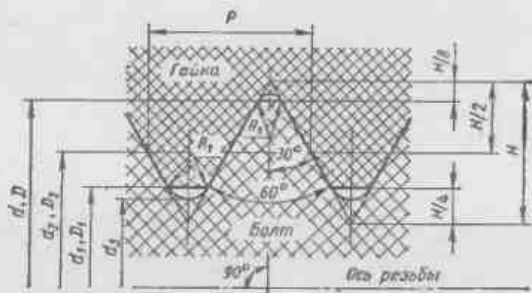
Профиль метрической резьбы деталей из пластмасс
